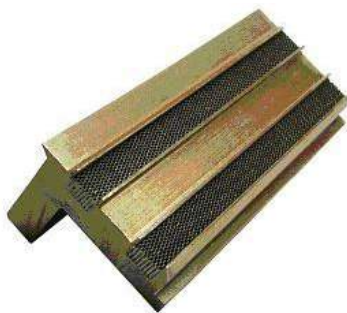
Внешний вид сотового надбандажного уплотнения для регулирующей ступени турбины ПТ-65/75-130
